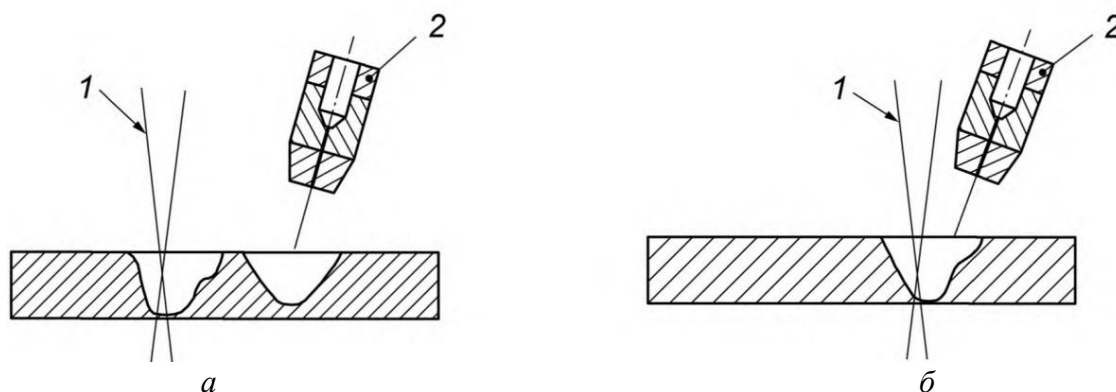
Примеры гибридного и комбинированного процесса: *а* – комбинированный процесс; *б* – гибридный процесс: 1 – лазерный луч 2 – сварочная головка
